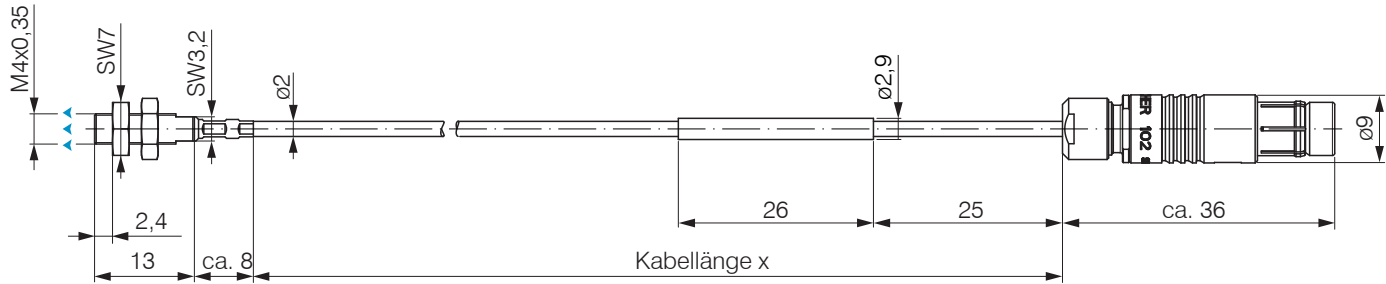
Maßzeichnung Sensoren ES-S04-CAx/mB0, Abmessungen in mm
